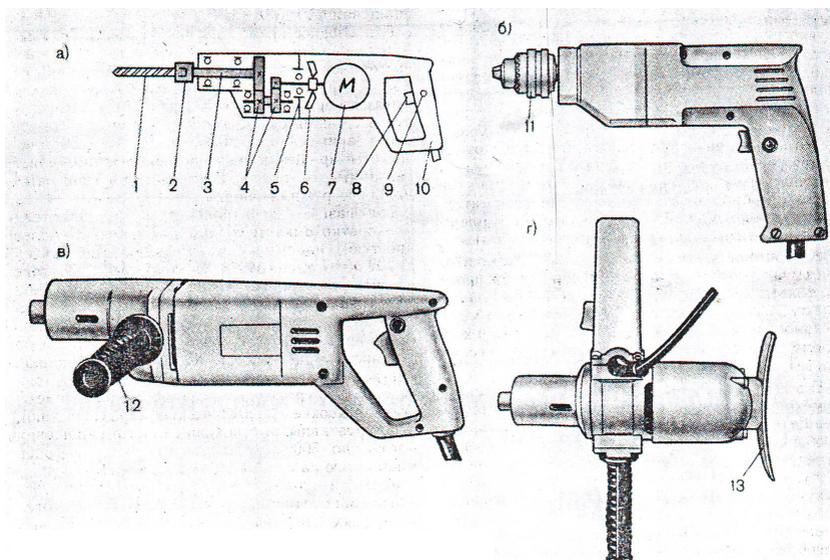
Сверлильная машина РМ: а – кинематическая схема; б, в – внешний вид; г – установка инструмента
